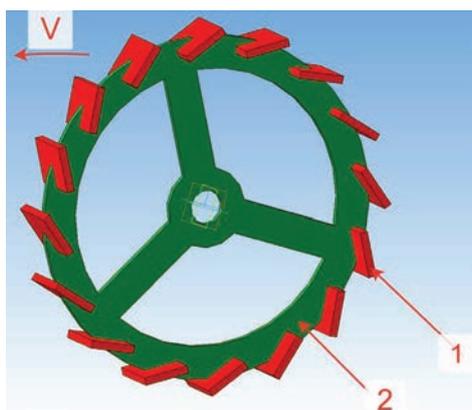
Конструкция кольчато-шпорового почвообрабатывающего рабочего органа:
